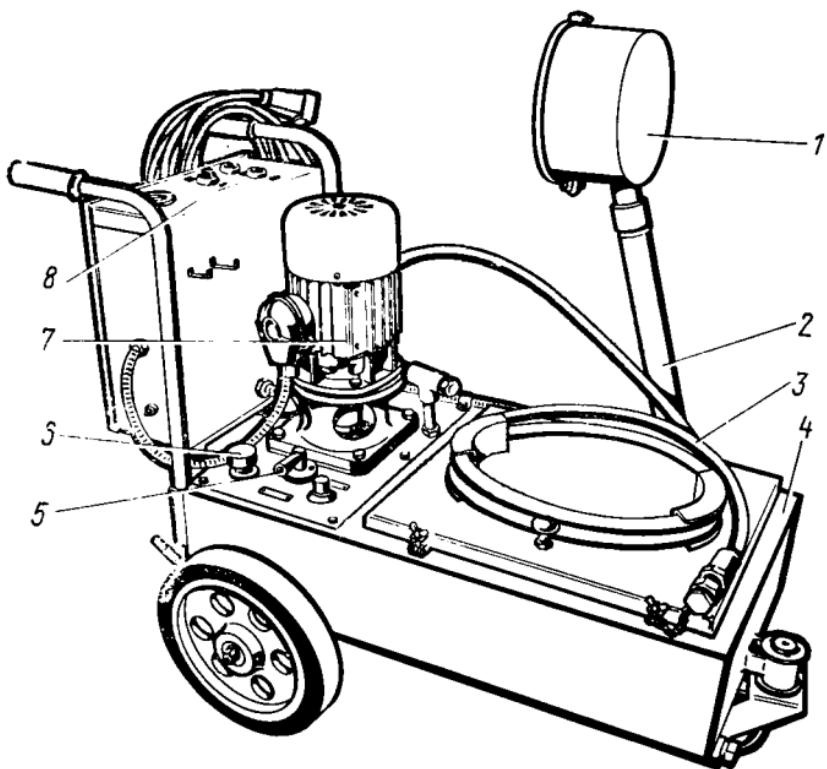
Установка ОМ-2871Б-ГОСНИТИ:
